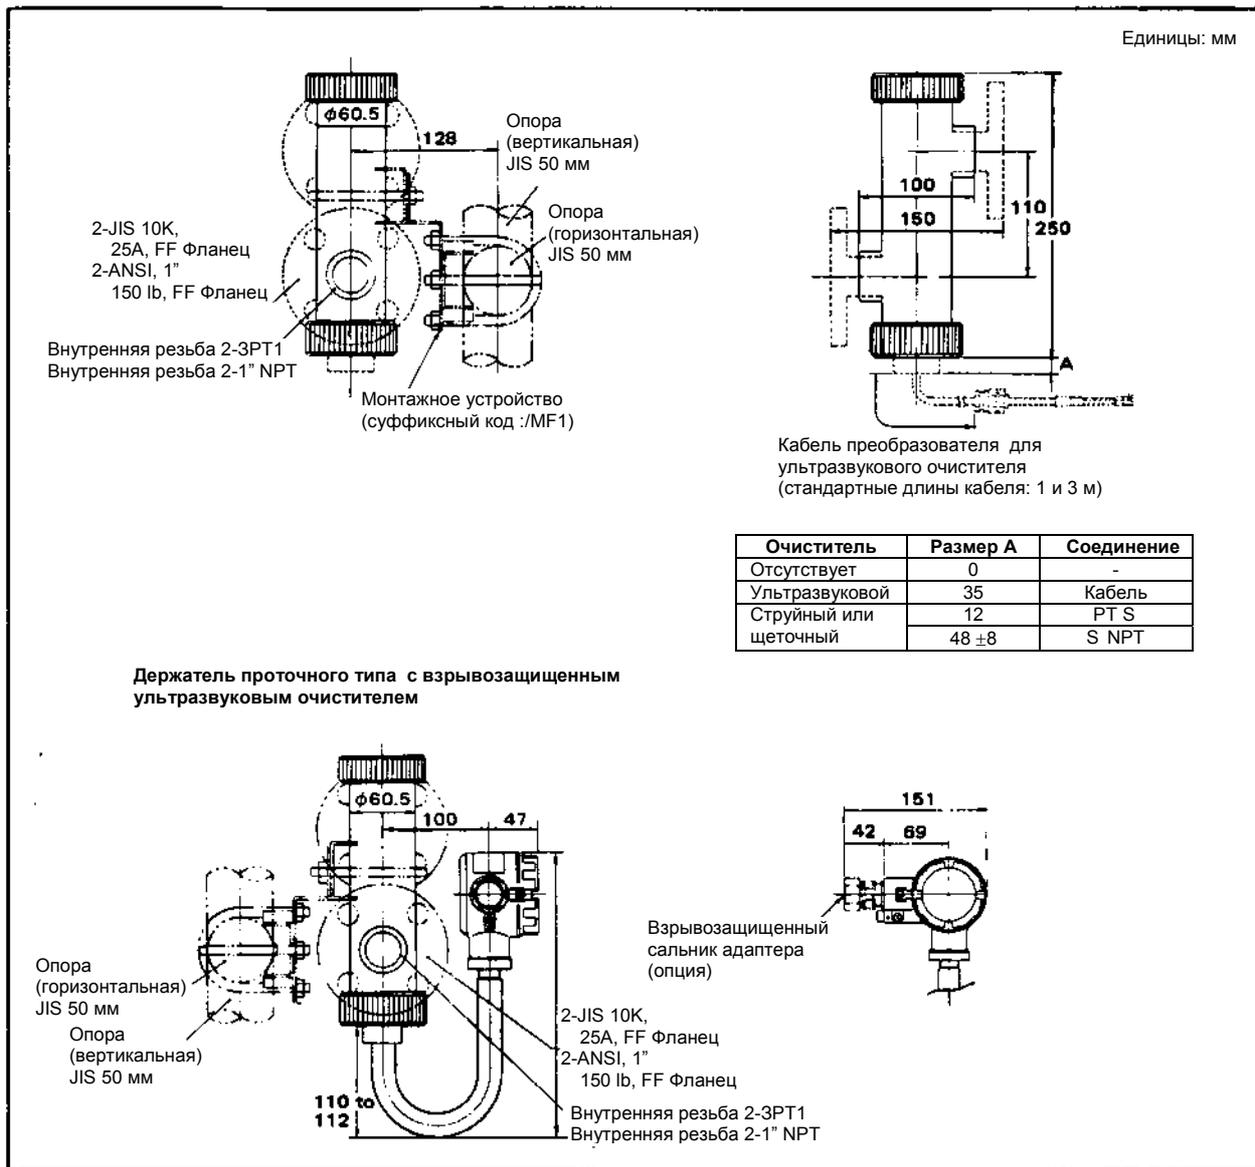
Держатель проточного типа – Внешние размеры
